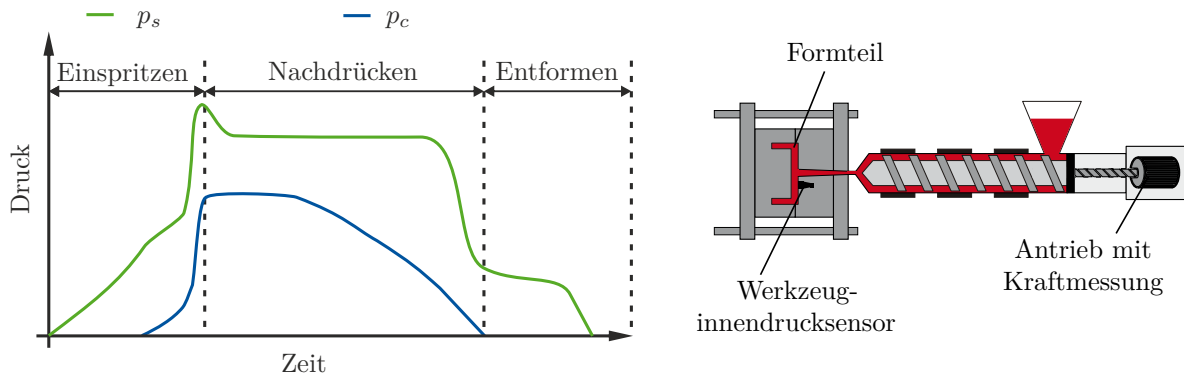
Schematische Darstellung der Verläufe des Schneckenorraumdrucks p_s und des Werkzeuginnendrucks p_c (links) bei Integration eines Werkzeuginnendrucksensors (rechts).
